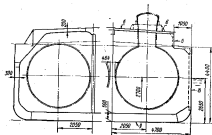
Поперечный разрез корпуса цистерны «Торона» Марк № 1а.
